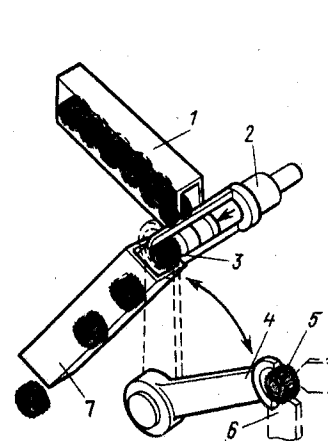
Рычажное устройство загрузки — разгрузки круглошлифовального станка
